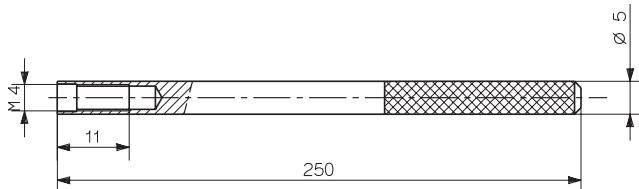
Ausziehwerkzeug für Blindsensor Typ 1319
